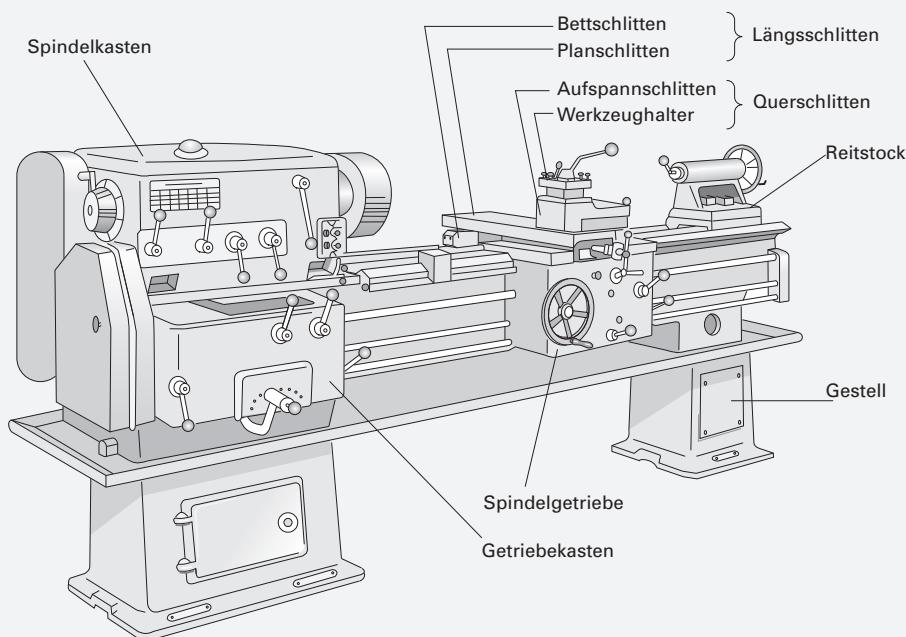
Drehmaschine, aus mehreren Baugruppen zusammengesetzt
